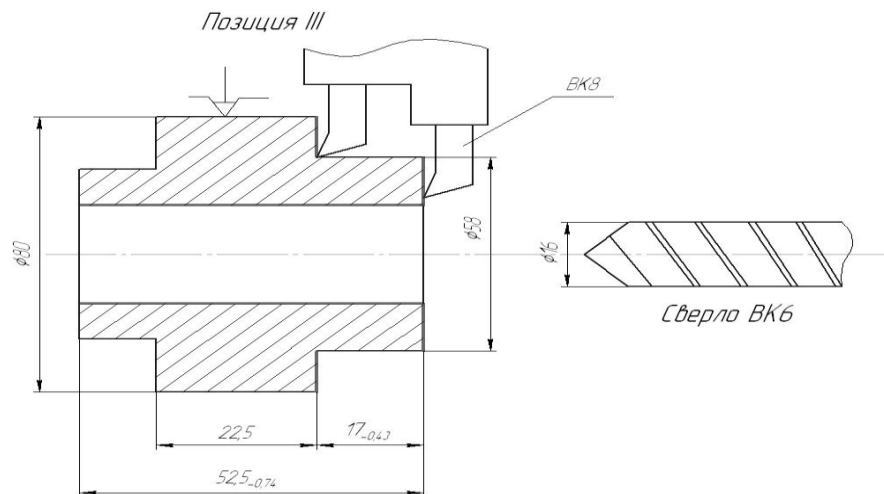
Сверление отверстия и подрезка торцов
